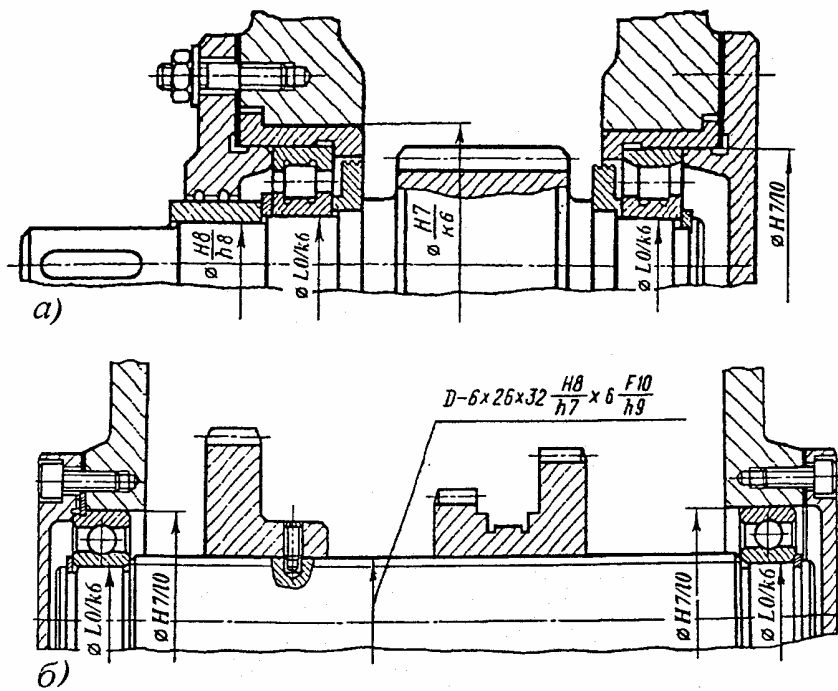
Установка радиальных роликовых и шариковых подшипников с фиксирующей и плавающей опорами
